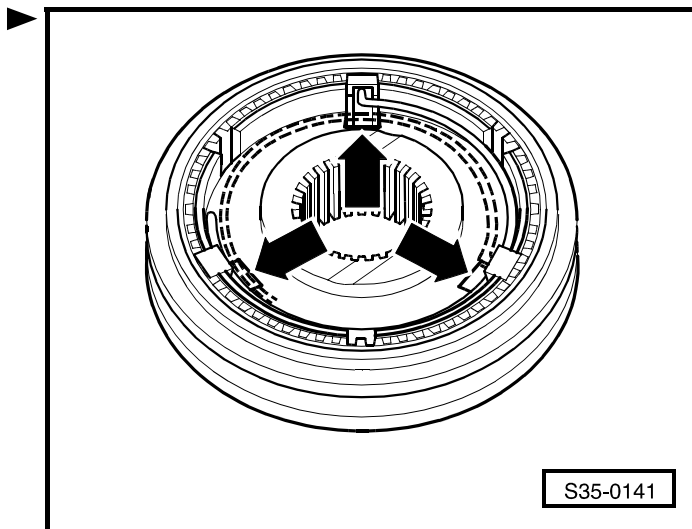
Положение для сборки скользящей муфты и каретки синхронизатора 3-ей и 4-ой передач
